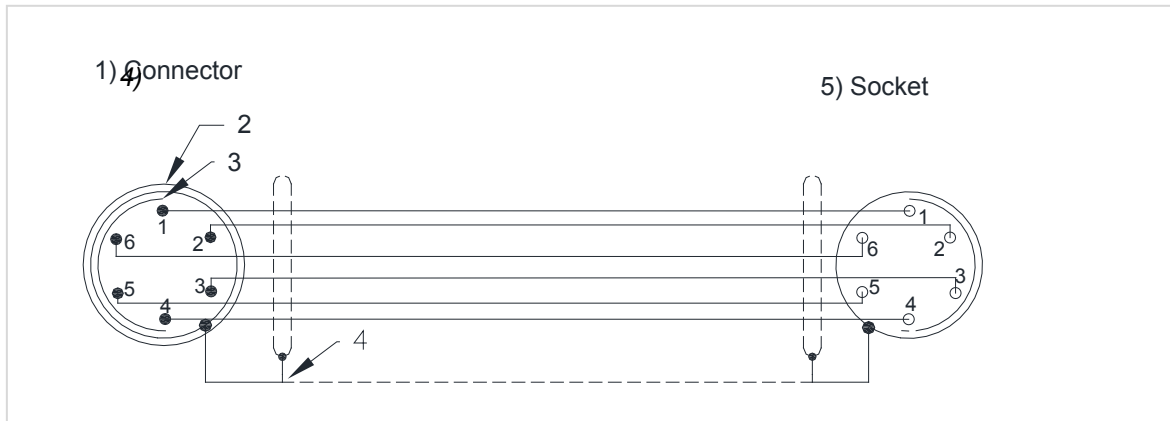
Anschlüsse Kabel - Blick auf die Steckseite / Connection Cable - View on connection/ Câble - Vue de côté de Connexion
